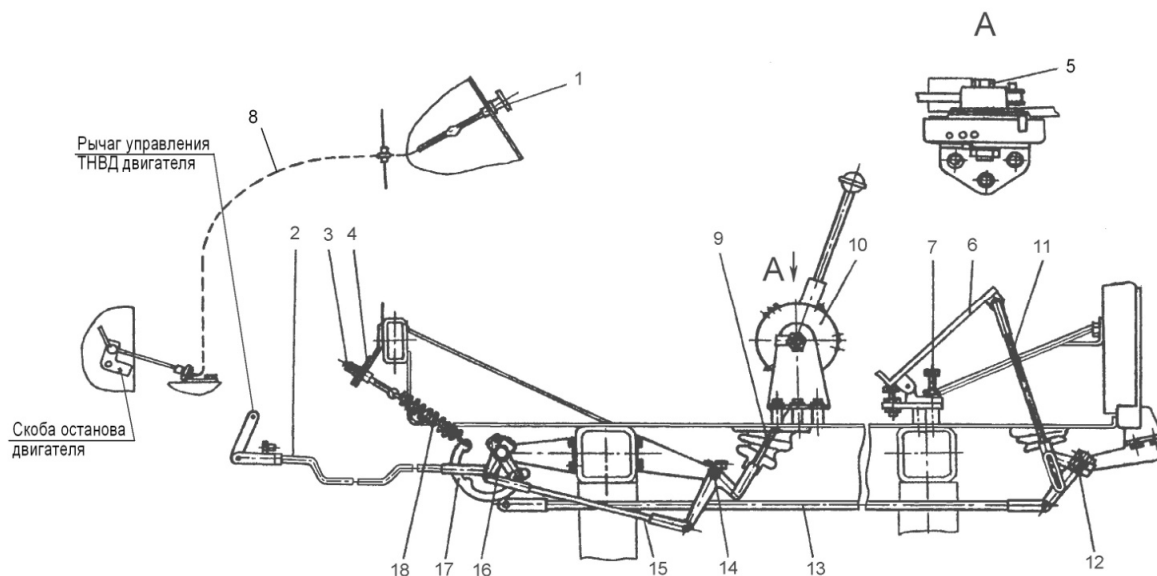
Схема привода управления подачей топлива и останова двигателя
